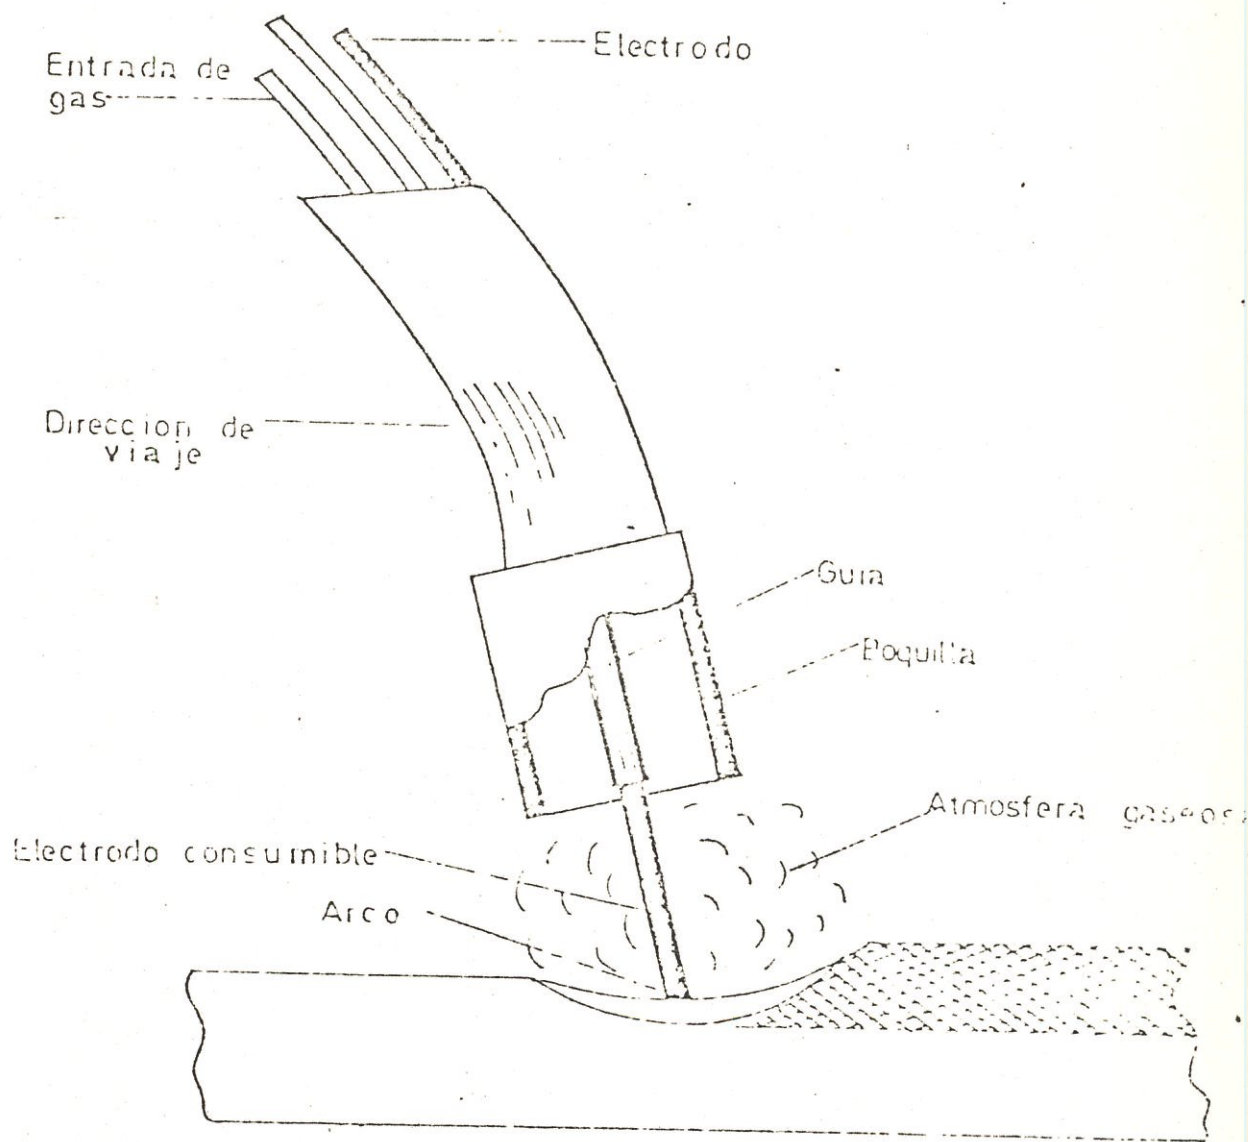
SOLDADURA AL ARCO EN UN PROCESO MIG (14)
